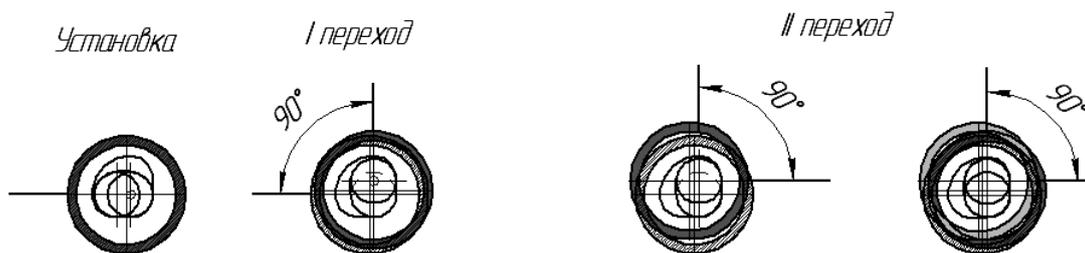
Первый и второй переходы процесса отрезания трубчатых заготовок сдвигом и скручиванием
